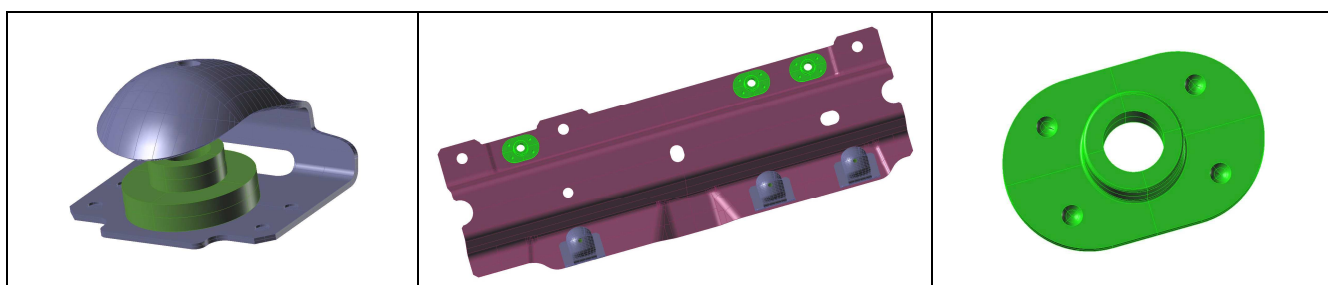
Elementi: Staffa – Elemento A8 - Boccola.
